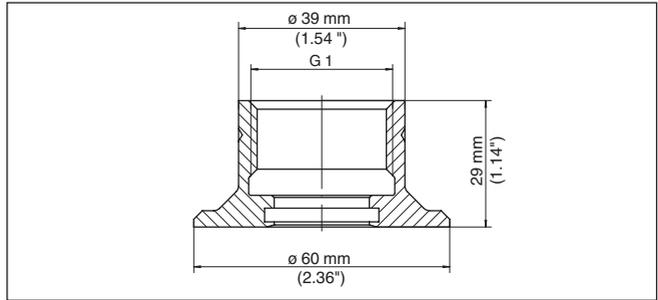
Medidas racor para soldar G1 (DIN 3852-X)
